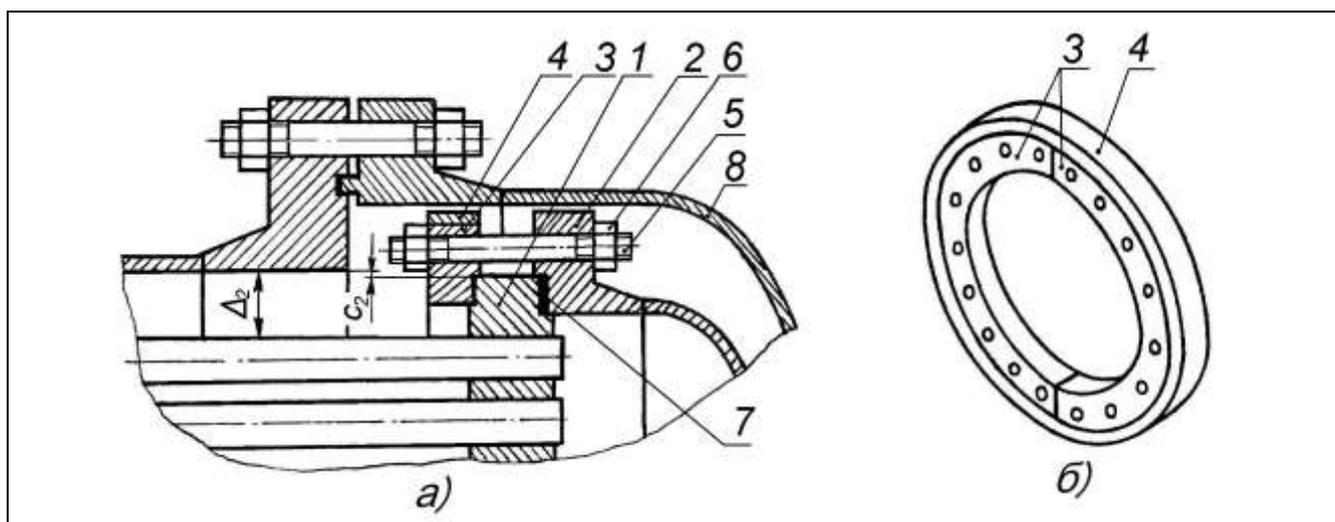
Плавающая головка типа П с разрезными фланцами 3 и наружным стяжным кольцом 4: а) – общий вид плавающей головки; б) – положение разрезных фланцев 3 с одетым на них наружным стяжным кольцом 4 перед сборкой крышки 2 плавающей головки аппарата
